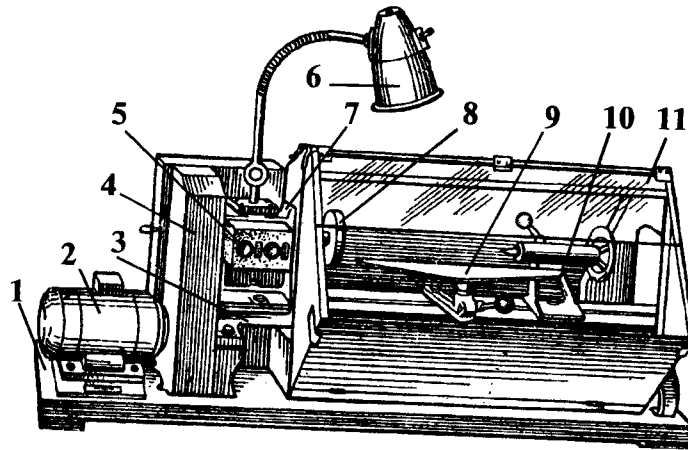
Токарный станок для обработки древесины СТД-120М:
